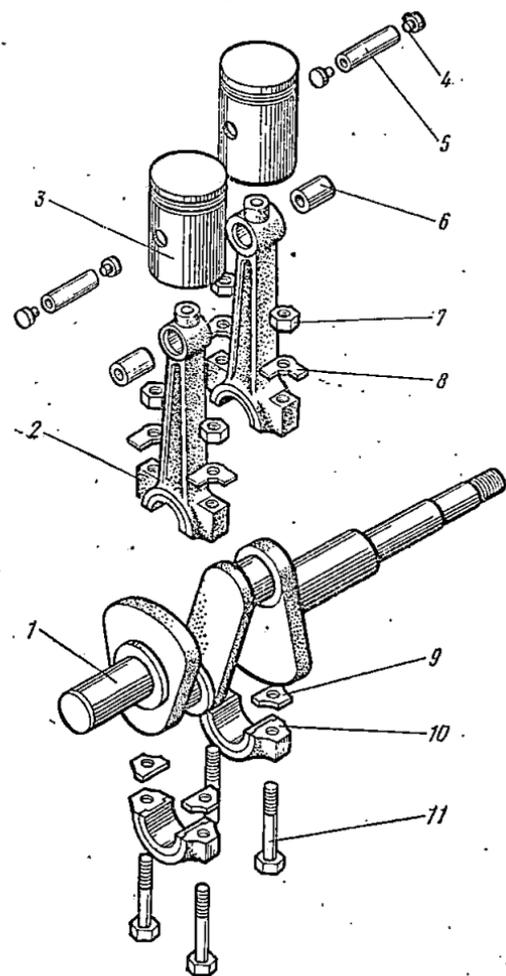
Кривошипно-шатунный механизм компрессора 2ФВ4/4,5:
